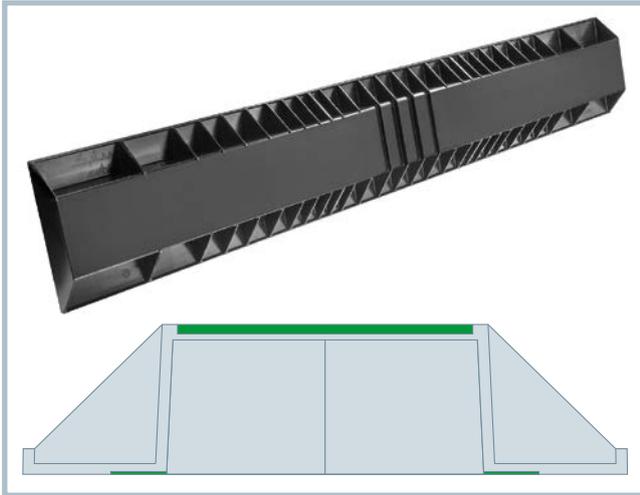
Musterbauteil mit drei unterschiedlich bemessenen UD-Laminat-Einlegern. Im abgebildeten Querschnitt (unten) sind die Einleger grün eingefärbt (© Sabic)
